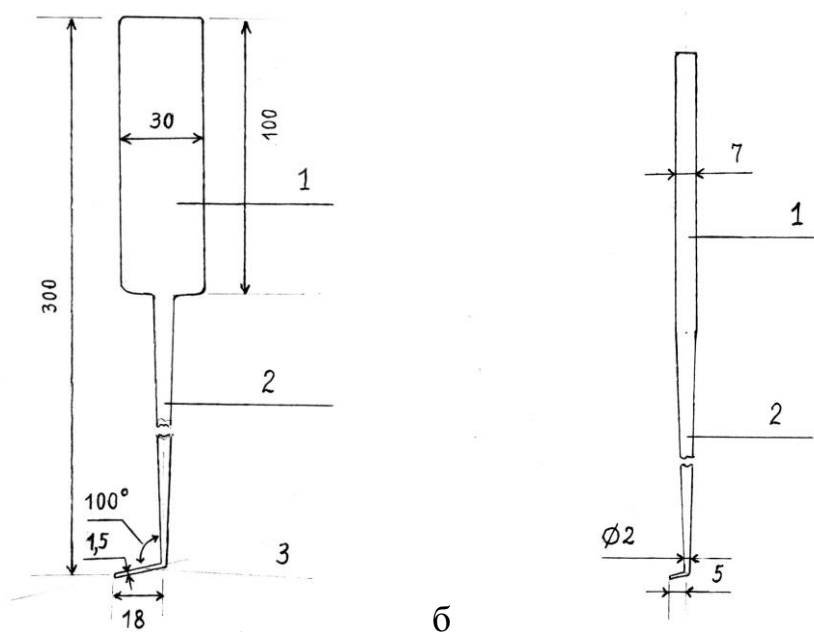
Схема инструмента для малоинвазивной декомпрессии позвоночного канала: а – вид сбоку; б – вид сверху
